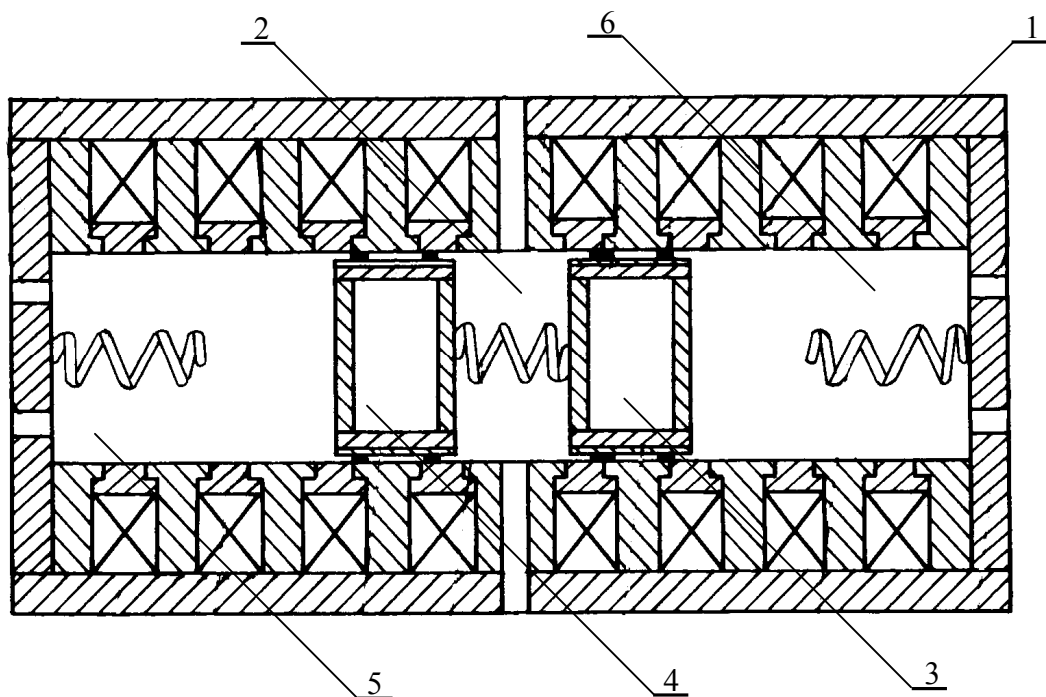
Свободнопоршневой электромагнитный компрессор
